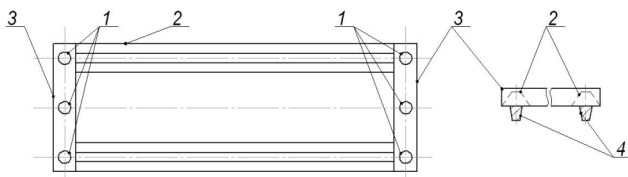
Рамная конструкция направляющих поперечного суппорта станка
